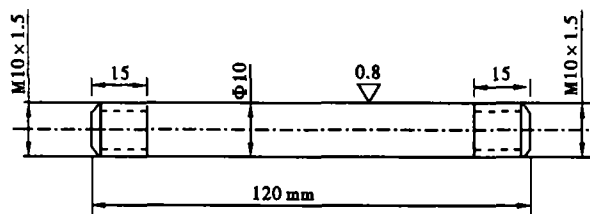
GCr15 轴承钢高温机械性能试样的尺寸
